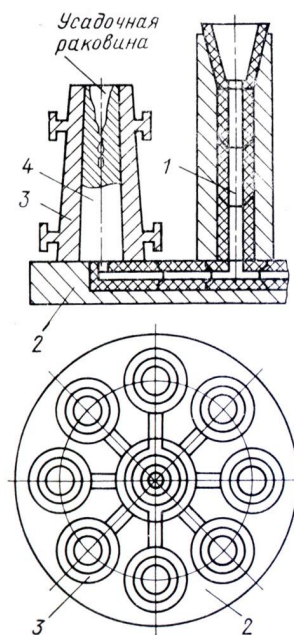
Схема сифонного заливання сталі: 1 – стрижень центрального стояку ливникової системи; 2 – піддон для встановлення восьми виливниць, 3 – виливниця, 4 – заготовка
